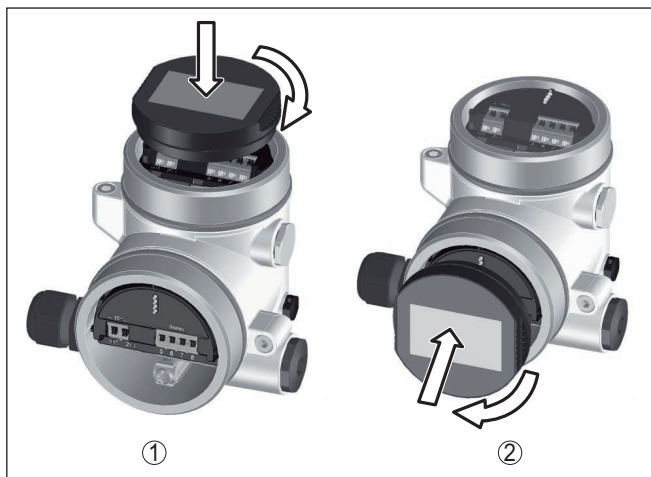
Установка модуля индикации и настройки в двухкамерном корпусе
